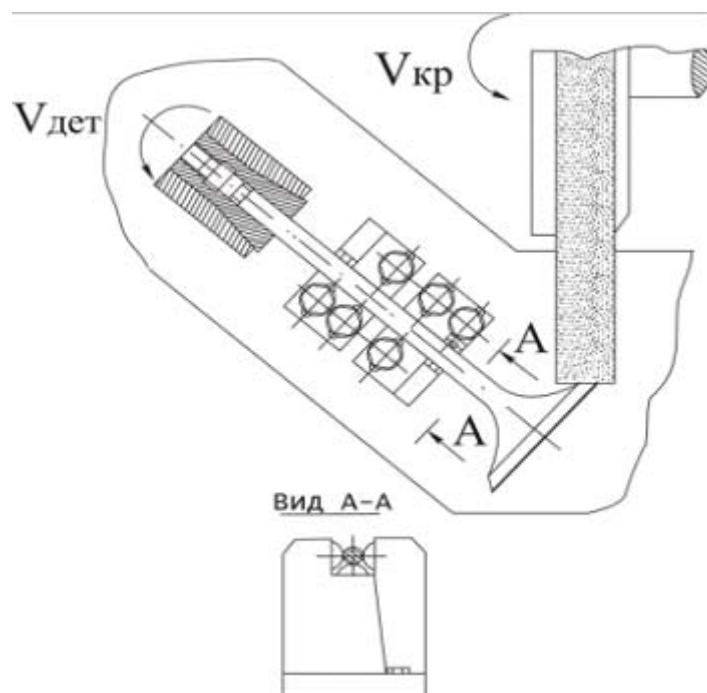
Приспособление для увеличения жесткости крепления клапана в приводе вращения станка
